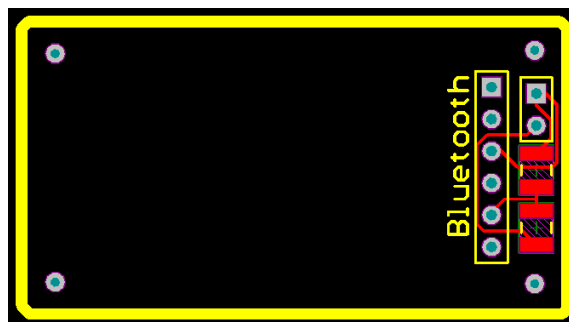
Circuito PCB diseñado para el módulo bluetooth.
